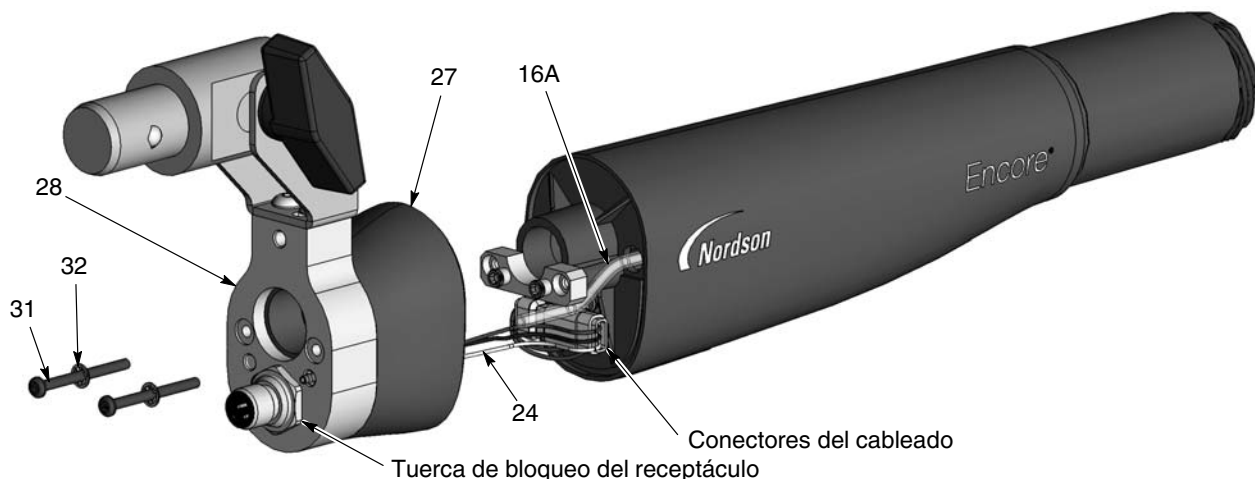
Desmontaje de la pistola - Sustitución del tubo de polvo
